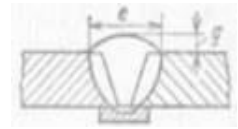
Сварной шов с подкладным кольцом
